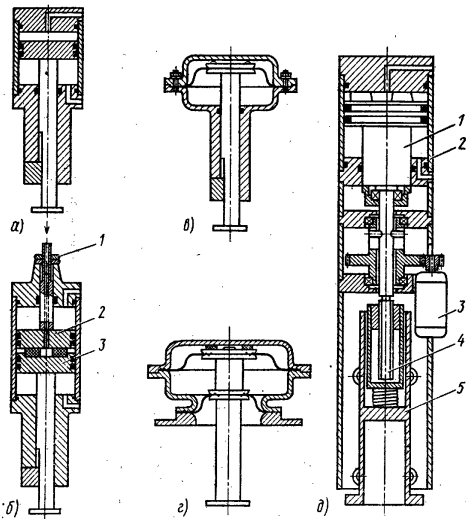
Пневматические приводы сжатия электродов для машин контактной сварки
